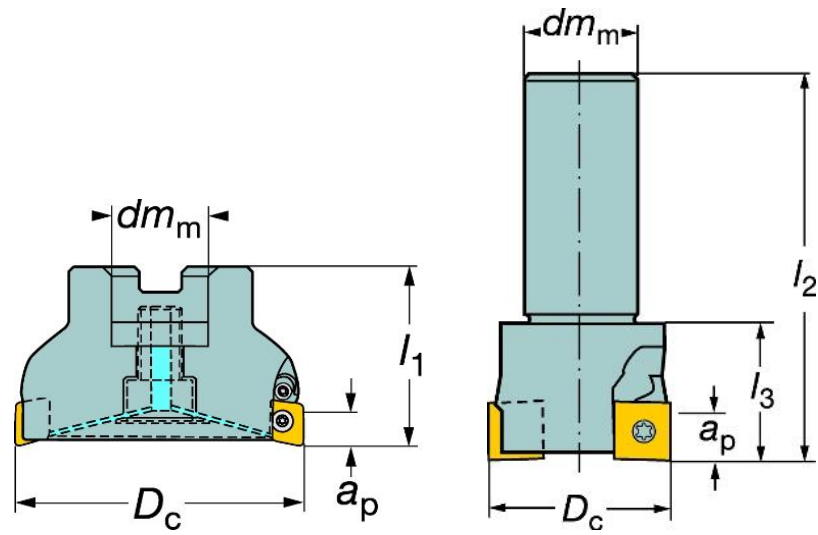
Фрези фірми SANDVIK COROMAND
